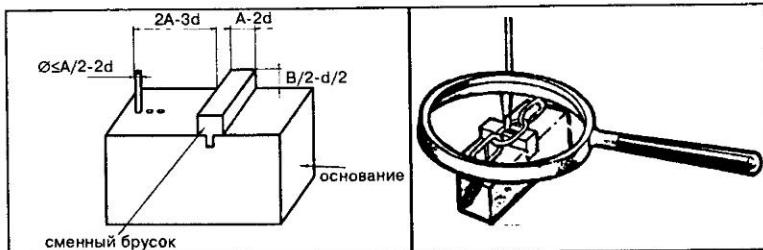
Приспособление для пайки звеньев якорной цепи:
